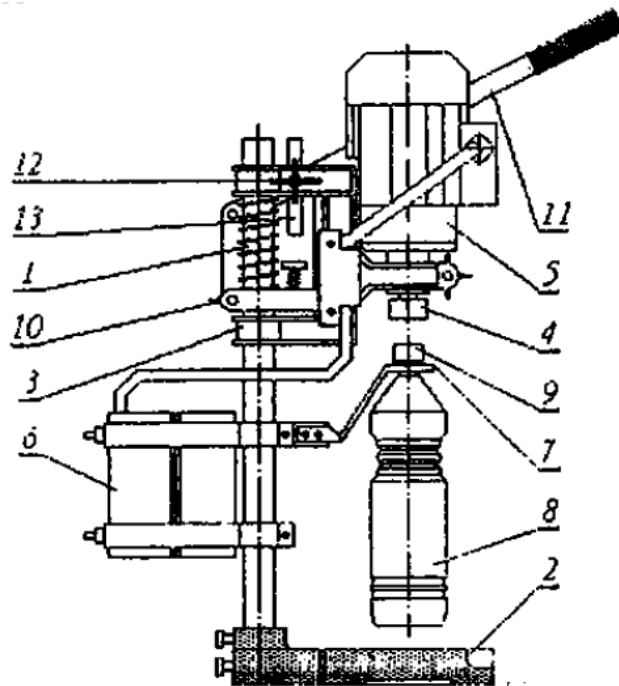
Напівавтоматичний пристрій закупорювання пляшок пластмасовими пробками різьбленням УУ-3: 1 – стійка; 2 – основа; 3 – механізм вертикального переміщення закупорювальної головки; 4 – закупорювальної головки; 5 – електродвигун; 6 – пускач електричний; 7 – вилка-тримач; 8 – ПЕТ-пляшка; 9 – пробка; 10 – регулювальний гвинт; 11 – важіль; 12 – гвинт; 13 – регульований упор
